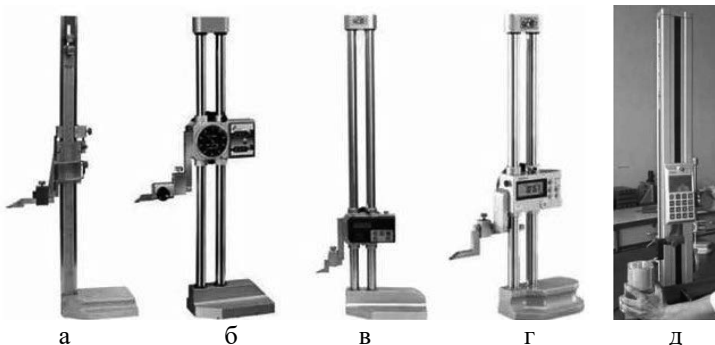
Штангенрейсмуси: а – механічний; б – вертикальний з індикатором годинникового типу; в, г – вертикальні з електричним індикатором; д – вимірювання висоти заготовки за допомогою електронного штангенрейсмуса
